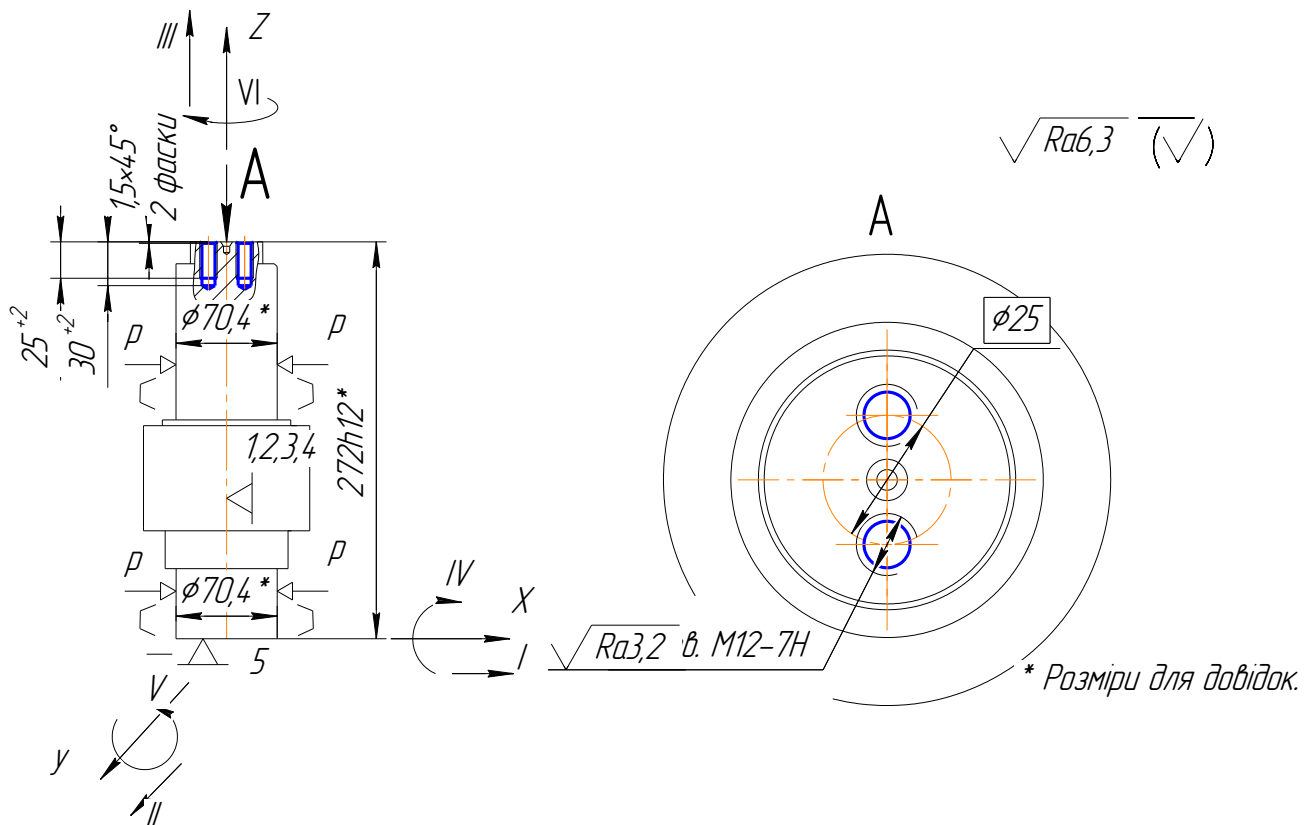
Схема базування заготовки на операції свердлильній
